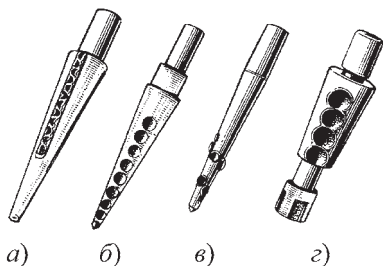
Конструкции поликристаллических катодов для АЭОПК твердосплавных волок:
